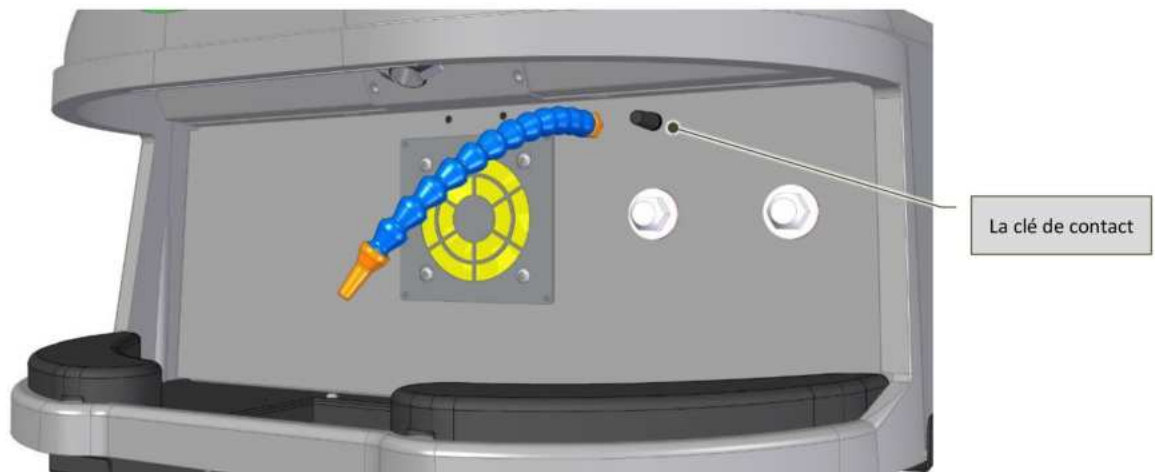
Clé de contact (vue intérieure de la chambre de soudage)
